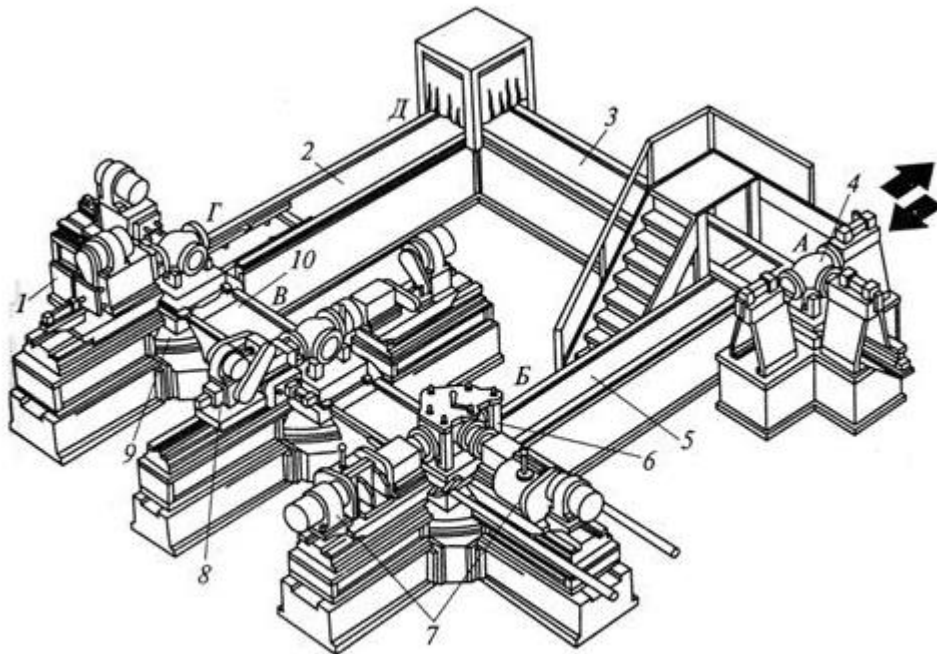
Однопредметная автоматическая линия для обработки корпуса клапана с приспособлением-спутником:
